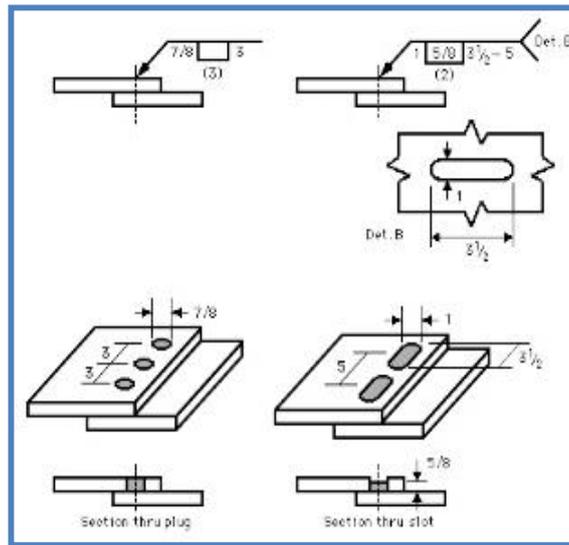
SOLDADURA DE TAPÓN
